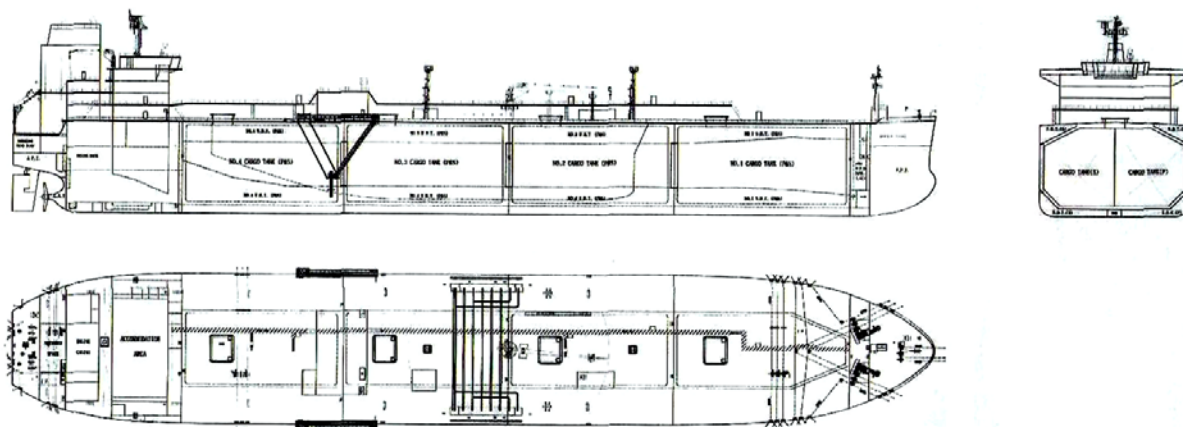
Загальний вигляд газовозу “CLIPPER QUITO”
